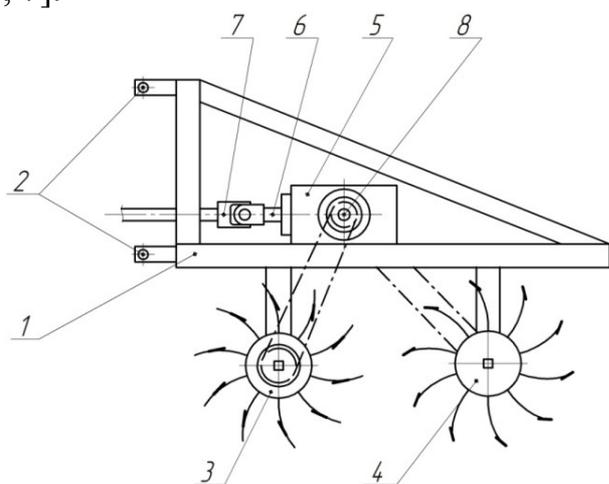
Тягово-приводное почвообрабатывающее орудие: 1 - рама; 2 - навесное устройство; 3,4 - игольчатые диски; 5 - конический редуктор; 6 - входной вал; 7 - карданный вал; 8 - выходной вал
